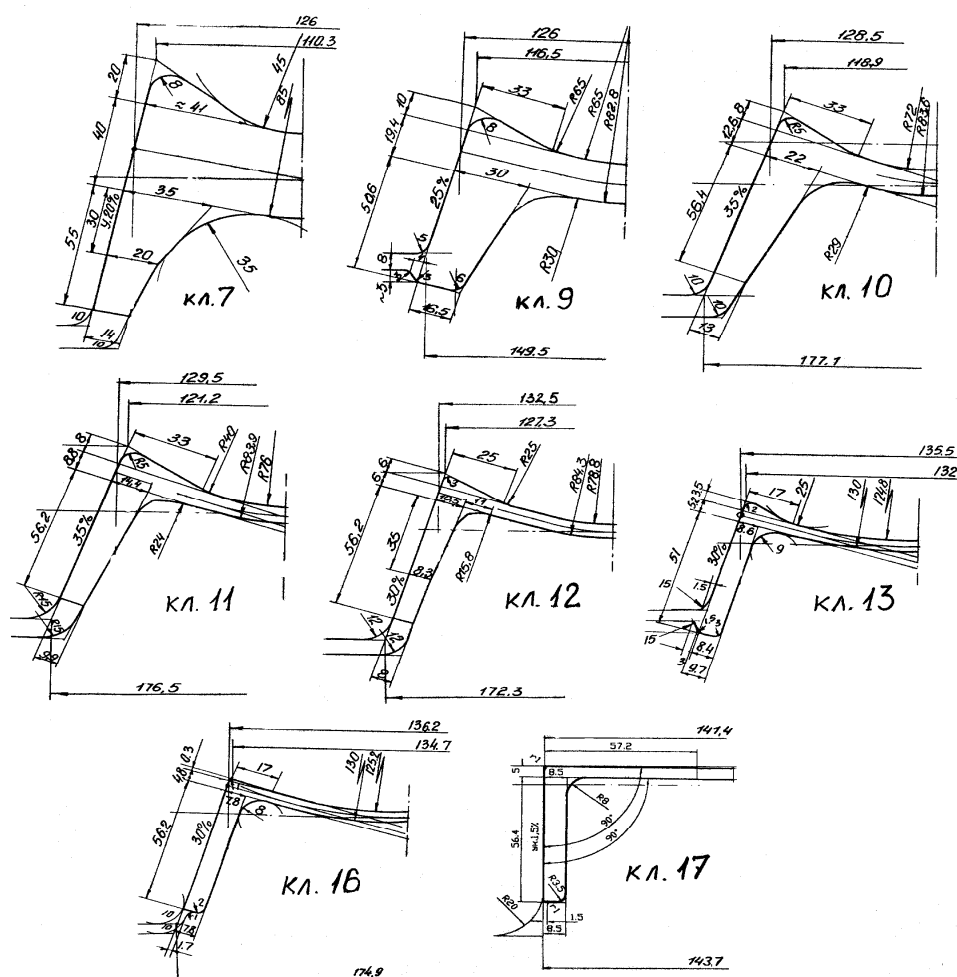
Разработанная калибровка швеллера № 14ПП
